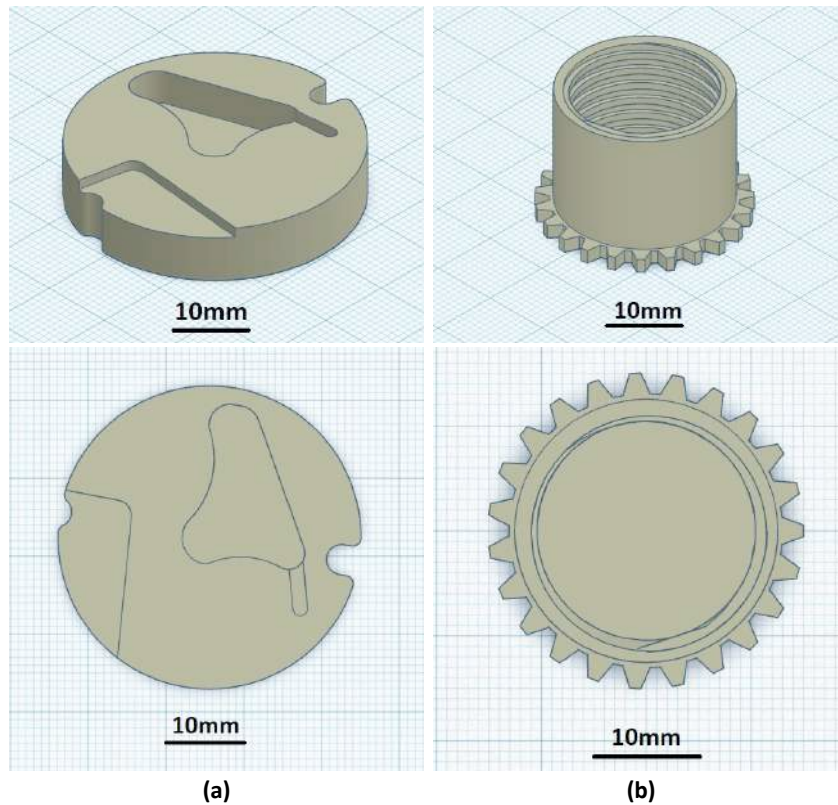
Modèles 3D des pièces produites - (a) valve et (b) insert denté.
